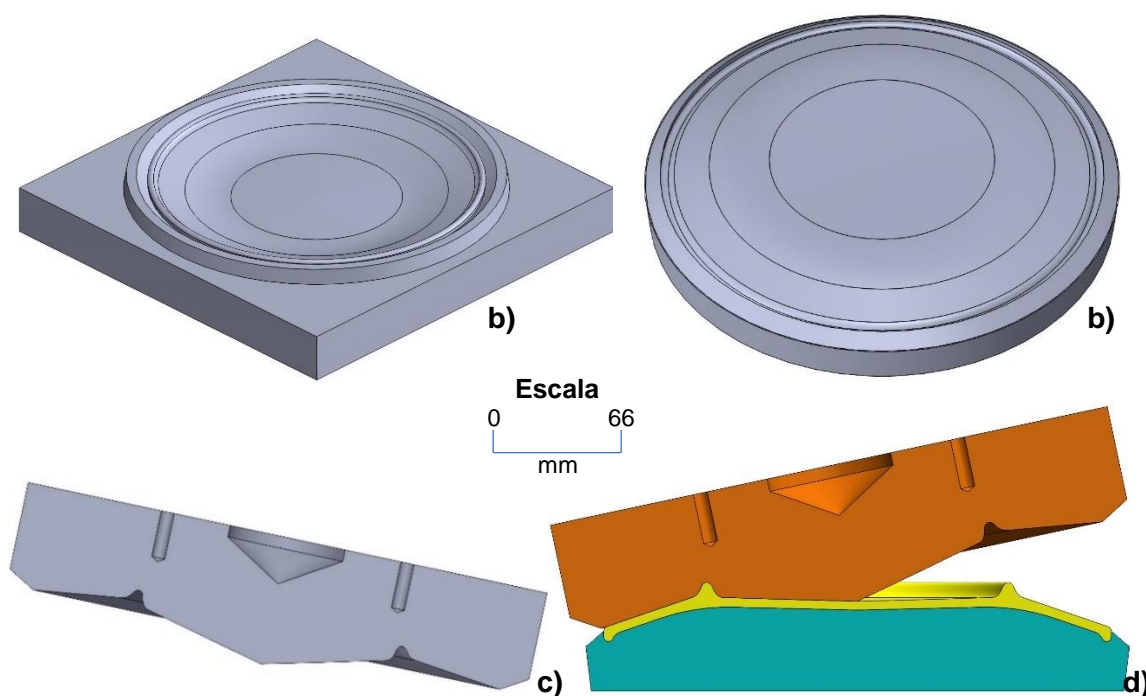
Componentes necessários para a conformação Roller do prato desenvolvido pela designer: a) madre; b) molde; c) calibrador e d) conjunto do molde, do prato e do calibrador.
